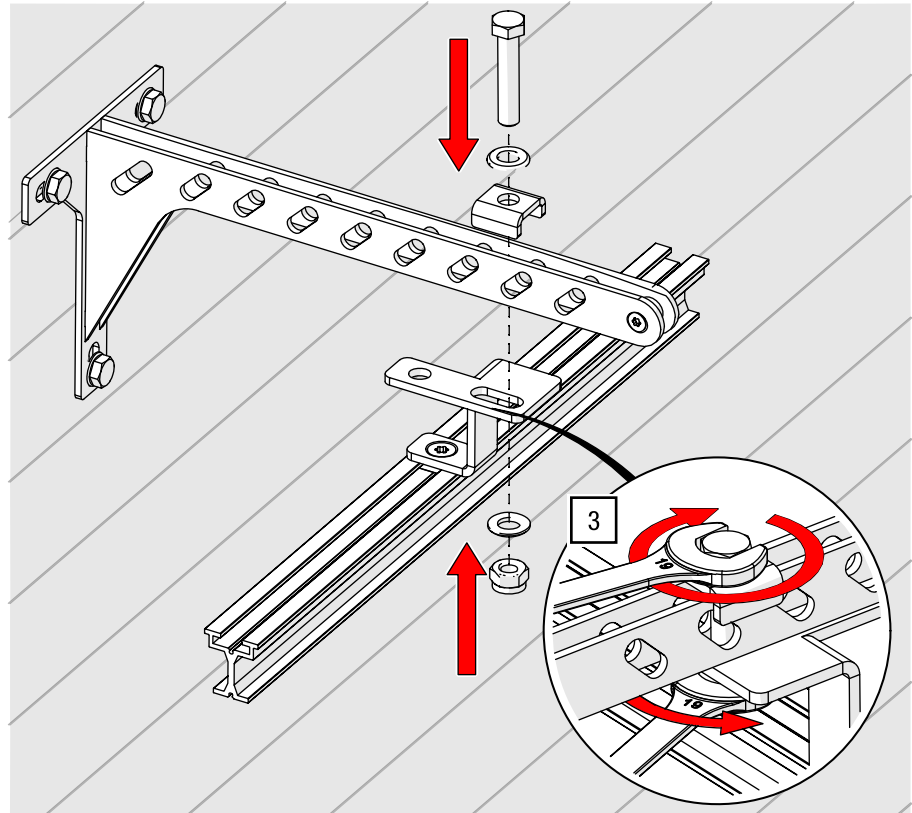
Wandarm mit Abhängung für Seilführung verschrauben
